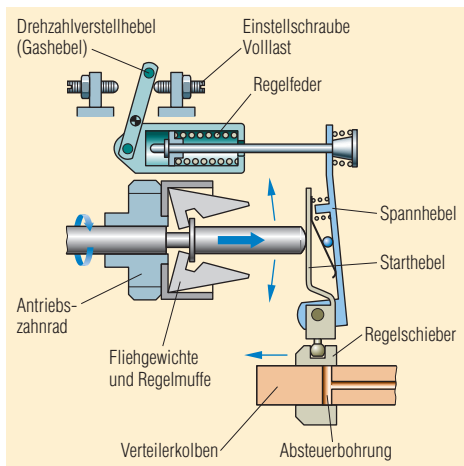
Mechanischer Drehzahlregler einer Axialkolbenpumpe.
